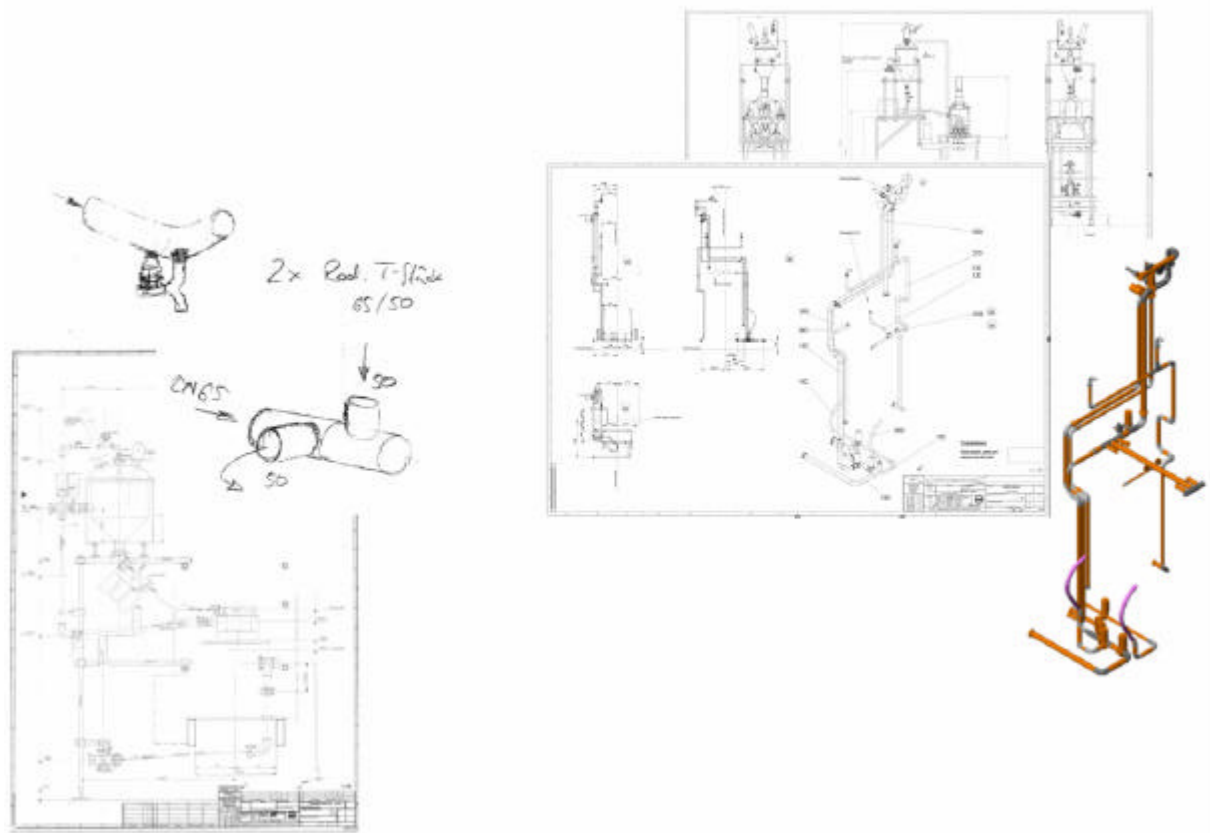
Produktzuführung (Verrohrung) einer Verpackungsmaschine
